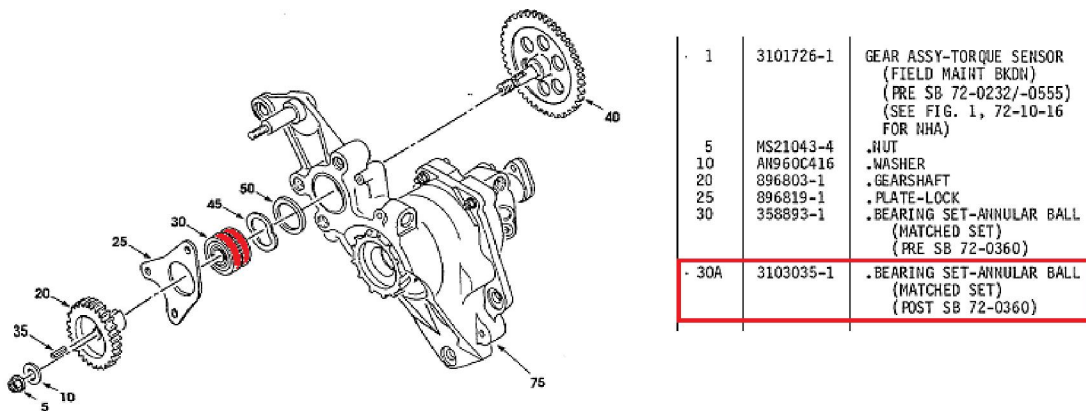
Ensamblaje de Generador de taquímetro y sensor de torque previo al SB 72-0232 (resaltado en rojo sobre el dibujo la primer versión del rodamiento en cuestión, recuadrado en rojo sobre la tabla la versión posterior al SB 72-0360).
